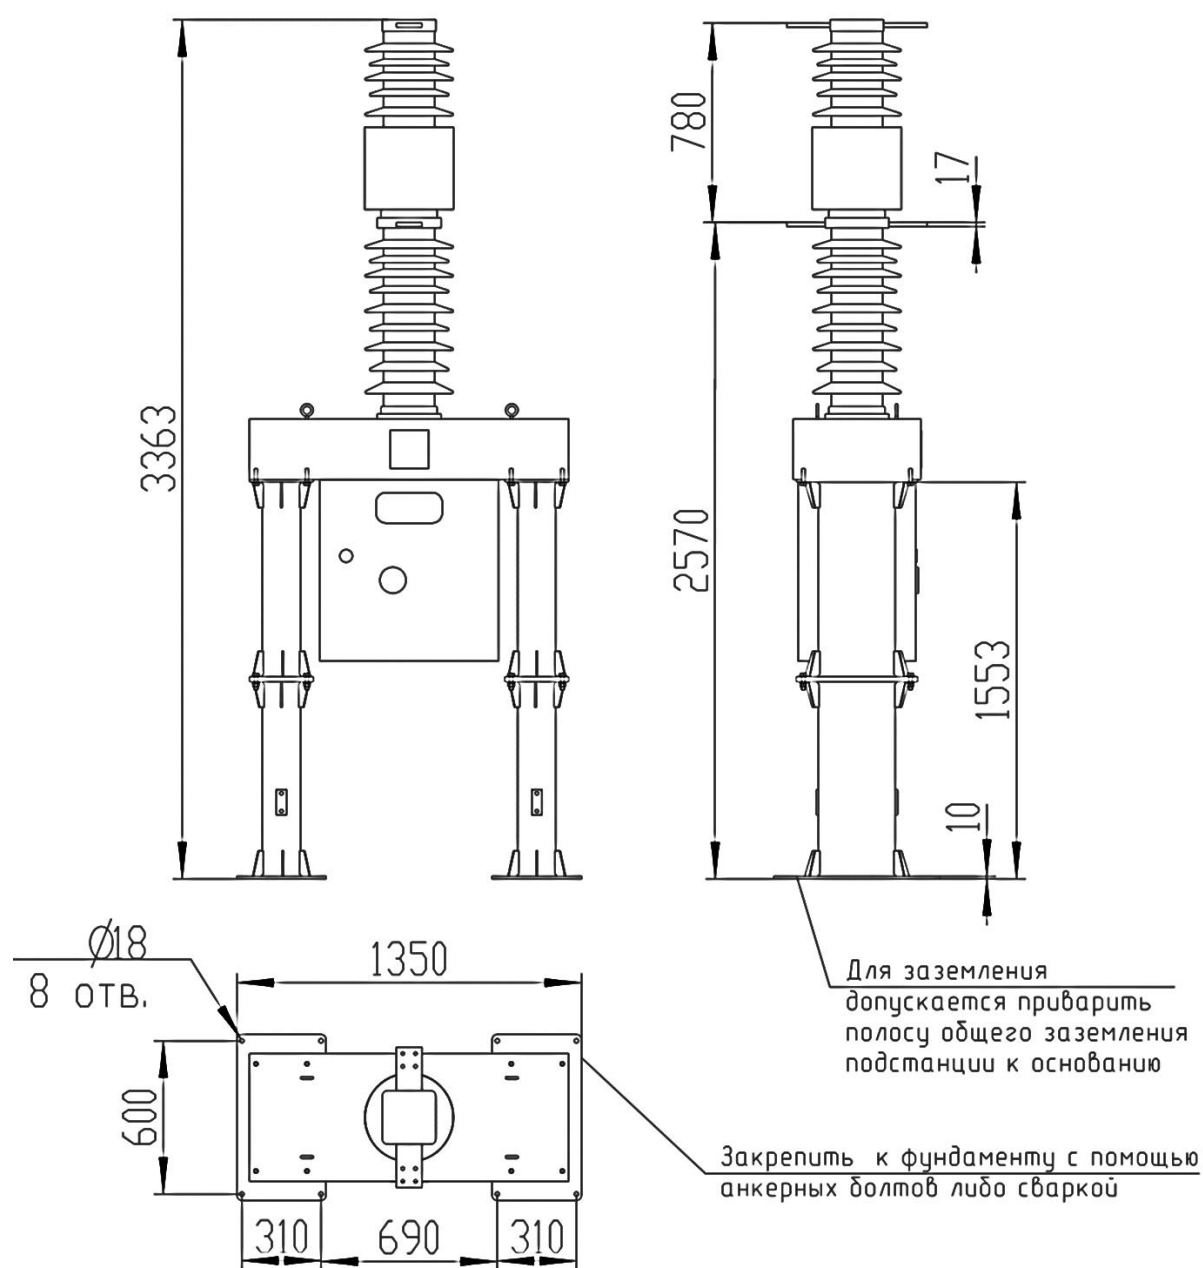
Габаритный чертеж выключателя высоковольтного
